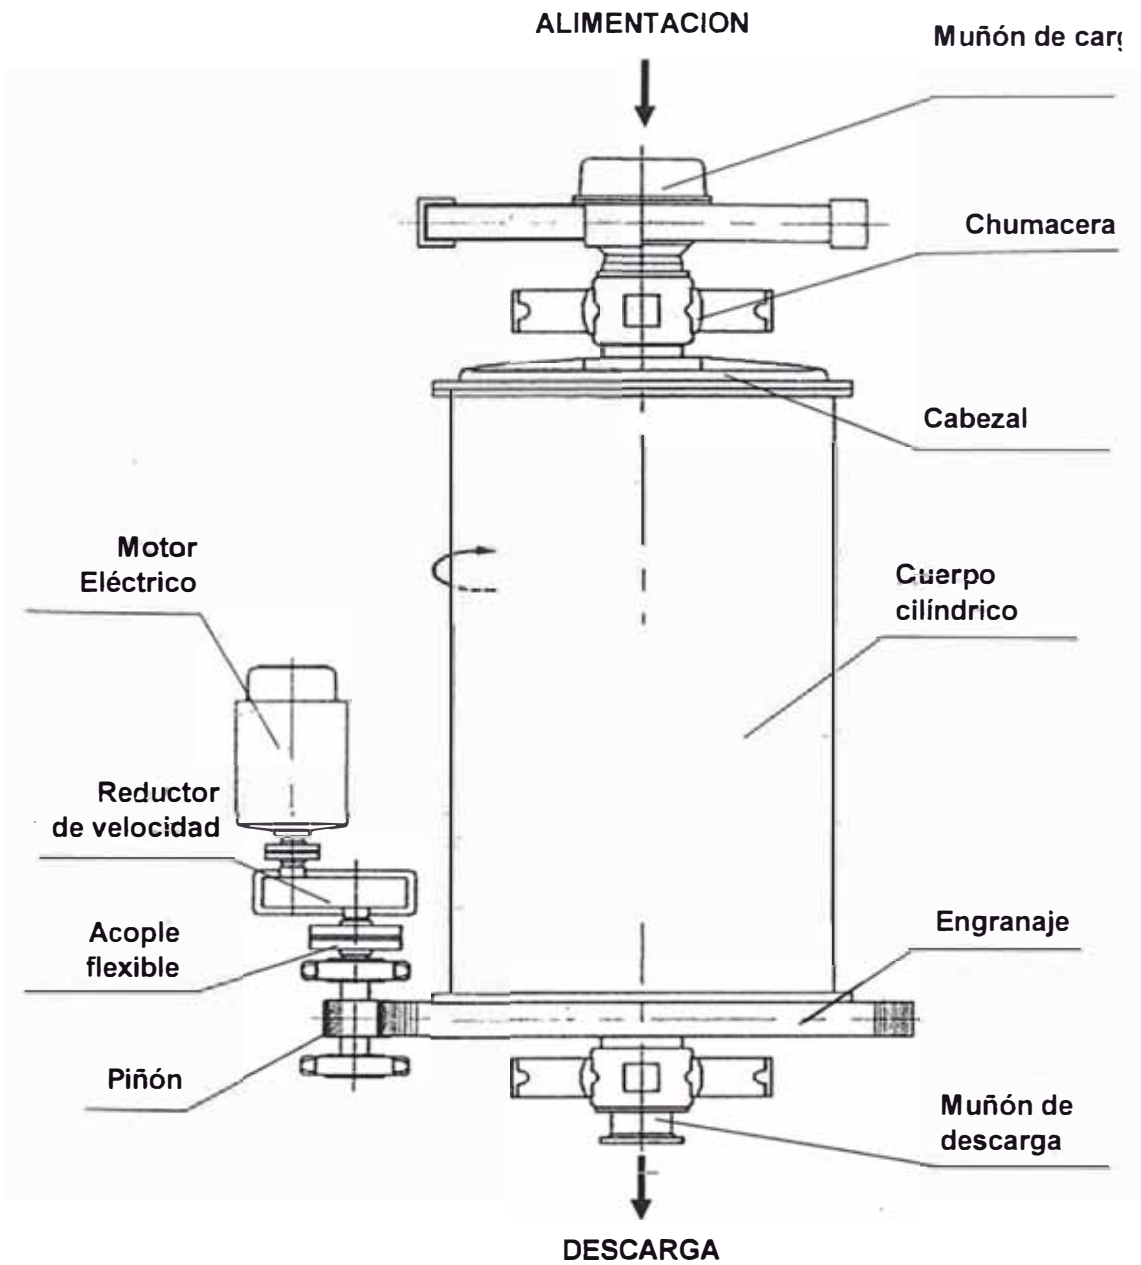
Molino de barras de 7'x12', montaje izquierdo.
